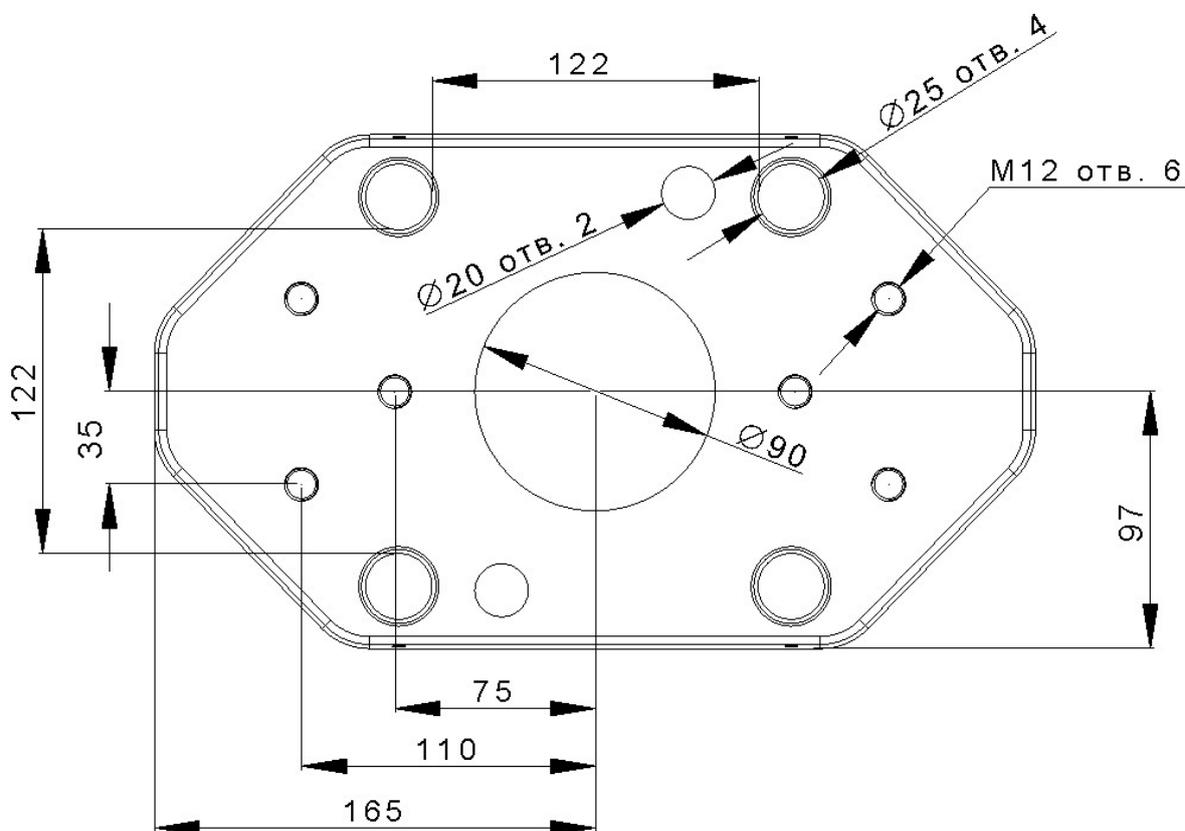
Плита крепления пресс-форм (правая) для «Formolder IMS-55»
